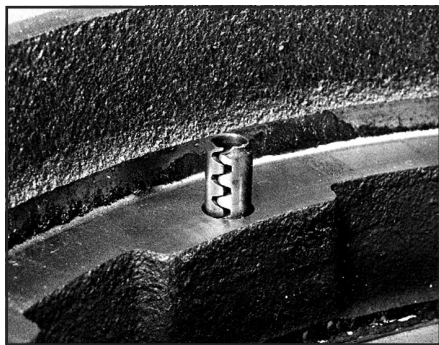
, б. Установочный штифт маховика для центровки нажимного диска
